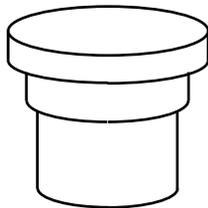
Bouton d'arrêt d'urgence avec mécanisme de bouton-poussoir
